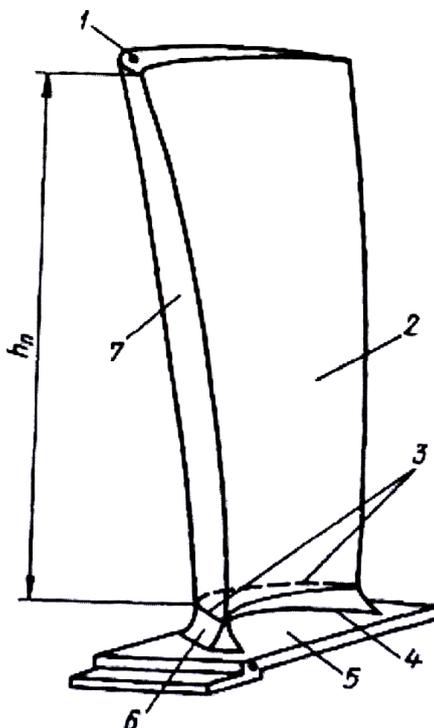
Перо лопатки с полкой хвостовика: 1 - торец пера; 2 - корыто; 3 - линия сопряжения переходной части лопатки с пером; 4- линия сопряжения переходной части лопатки с полкой; 5 - полка хвостовика; 6- переходная часть пера; 7- спинка; h_m , - высота пера.
